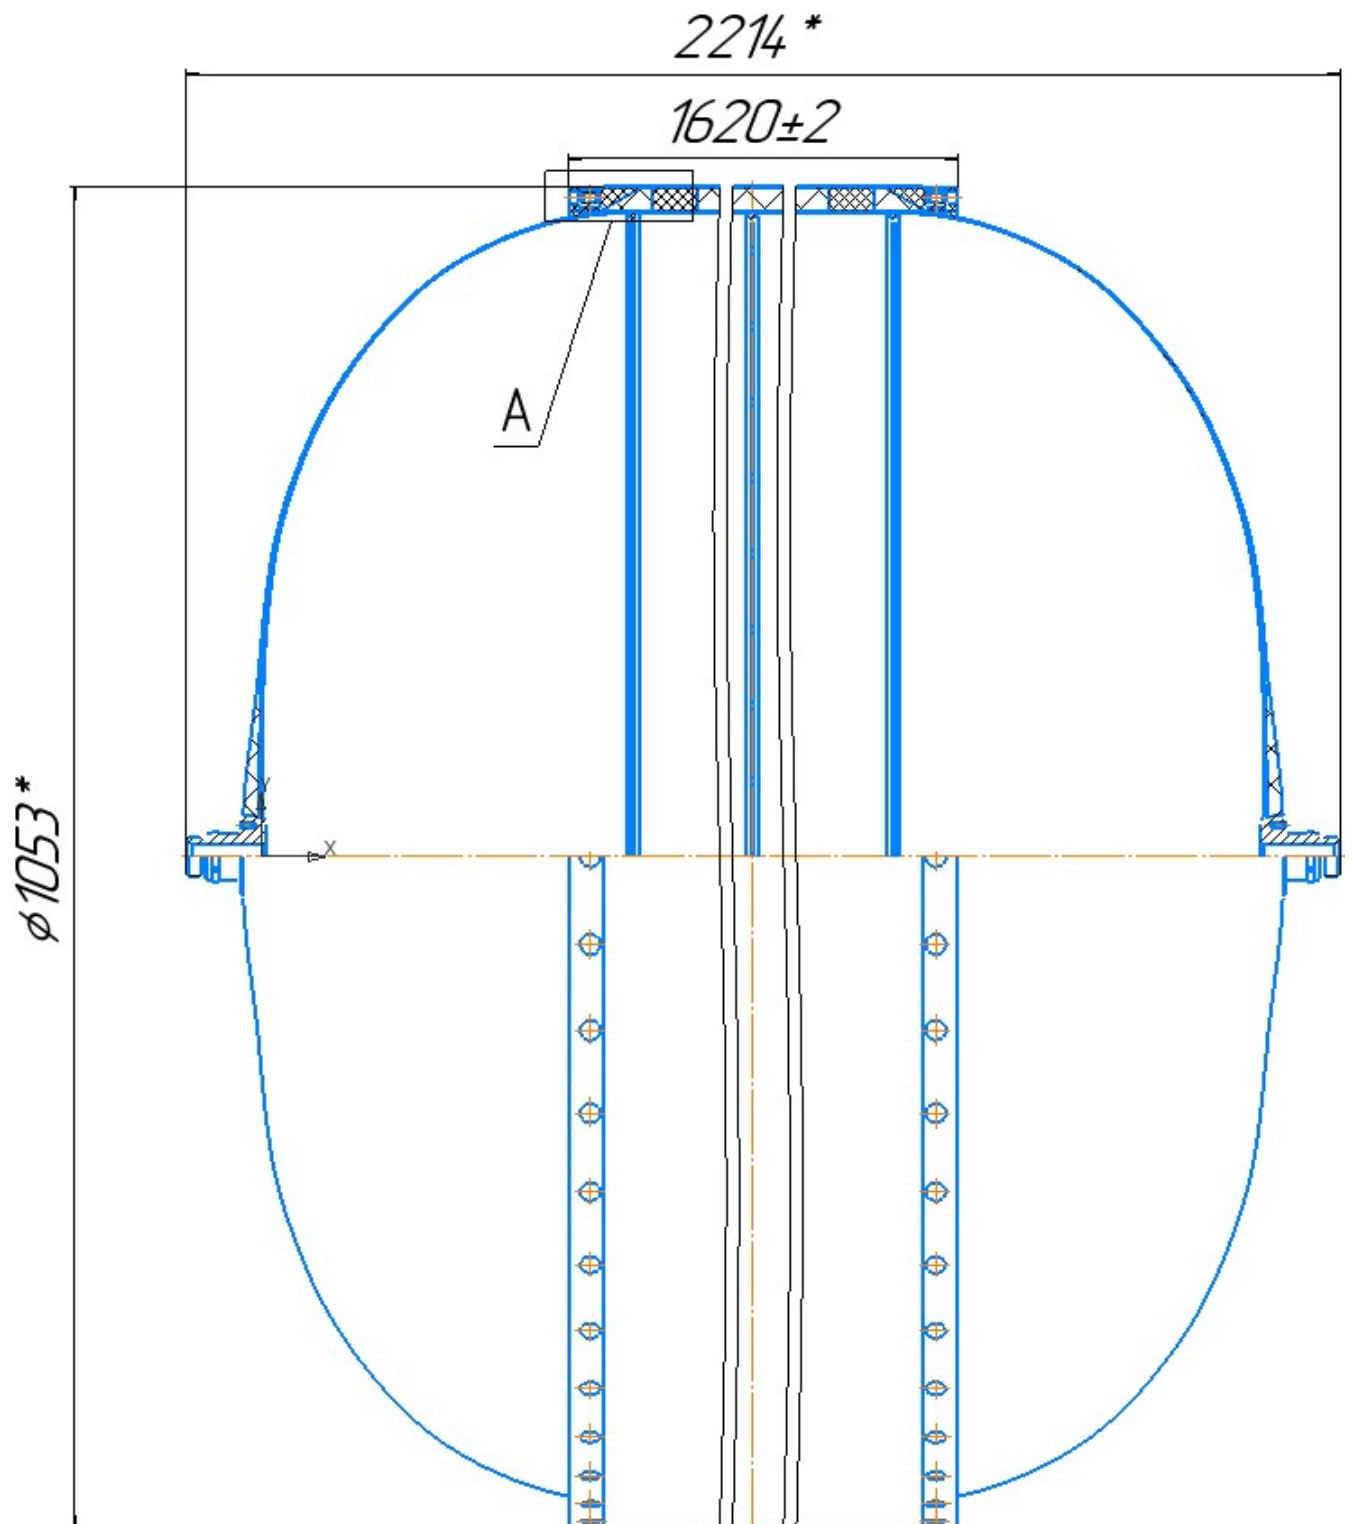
Общий вид и габаритные размеры модельного бака
